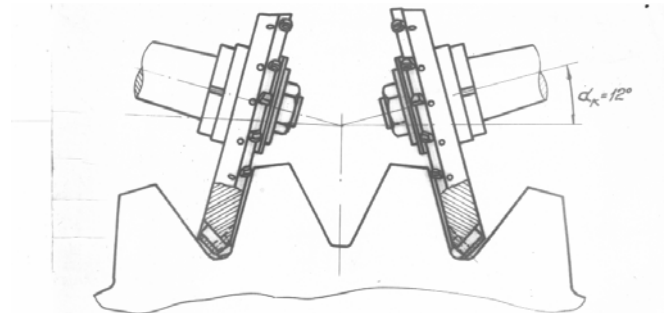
Схема чистовой обработки прямозубых колес торцевыми твердосплавными фрезами на спецсуппорте к станку мод. КУ-279
